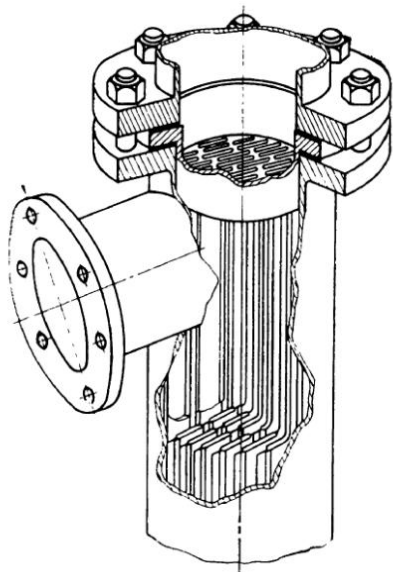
Узел соединения плоско-трубного пучка с трубной решеткой и корпусом
